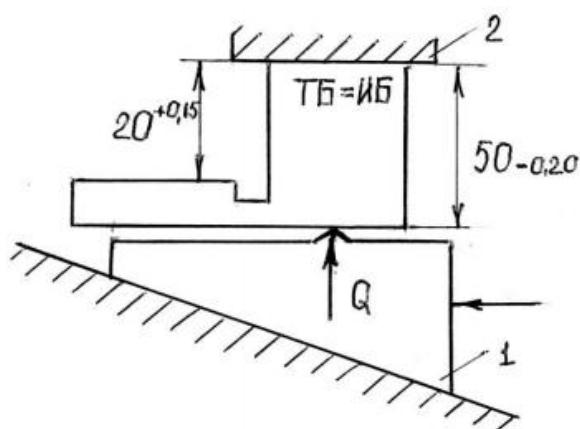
Схема станочного приспособления: 1 – клин, 2 – неподвижный упор
